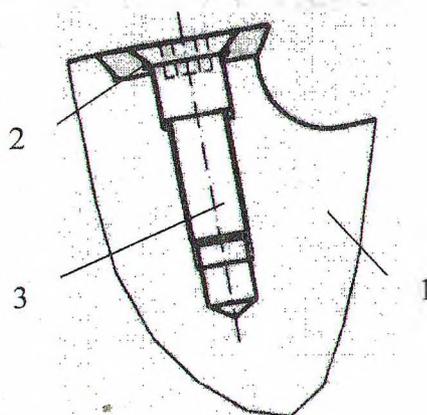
Способ крепления неперетачиваемых пластинок: 1 – корпус фрезы; 2 – неперетачиваемая пластинка; 3 – крепежный винт
